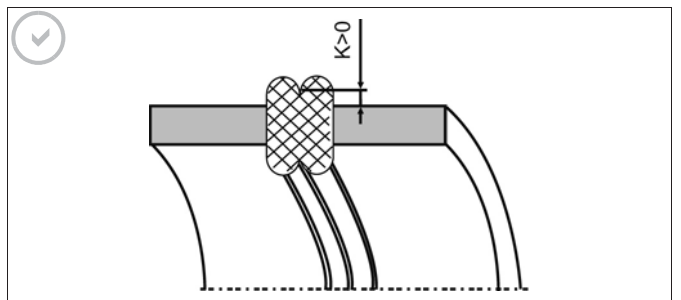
Поперечный разрез правильного стыкового шва
